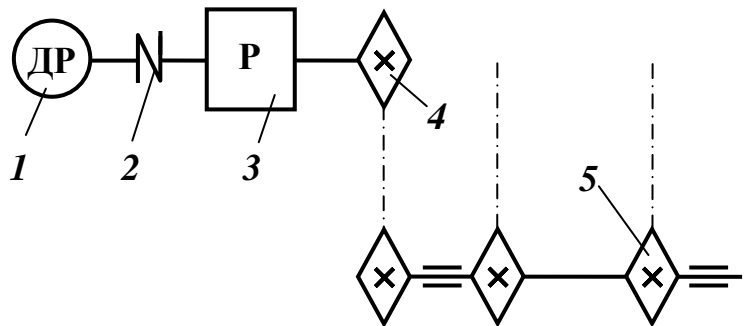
Схема приводу пастеризатора: 1 – двигун-редуктор; 2 – муфта; 3 – редуктора; 4 – ланцюгова передача; 5 – ведучий вал конвеєра з зірочками
